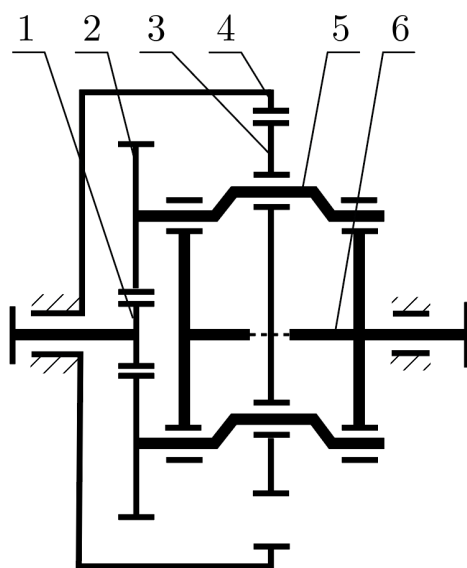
Планетарно-цевочный редуктор по схеме $2K-V$: 1 – солнечная шестерня; 2 – сателлит эвольвентной ступени; 3 – сателлит циклоидальной ступени; 4 – обойма с цевками; 5 – эксцентрик; 6 – выходной вал
